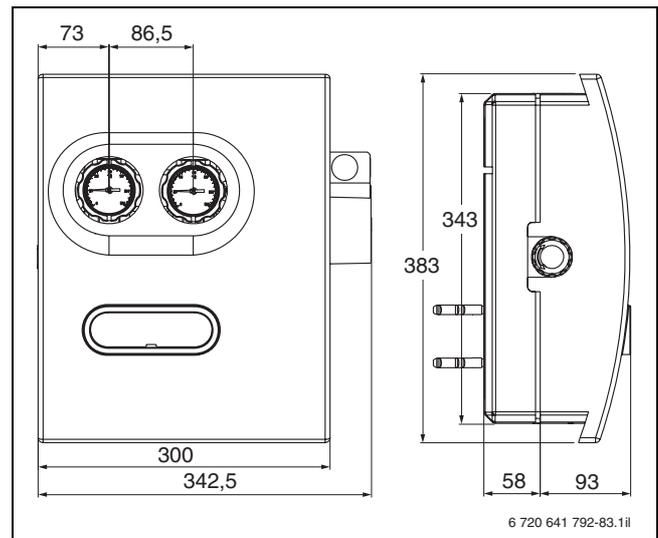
Abmessungen Warmwasser-Mischergruppe mit Zirkulationspumpe (Maße in mm)
